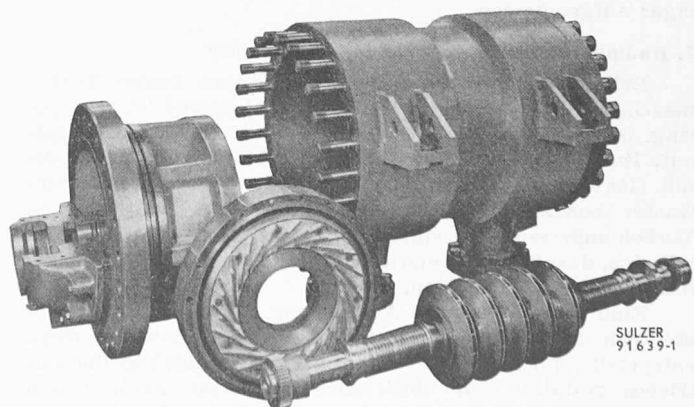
Fünfstufiger Turbokompressor, Typ RCX-5N-33,5, mit einteiligem Gehäuse für hohe Drücke
